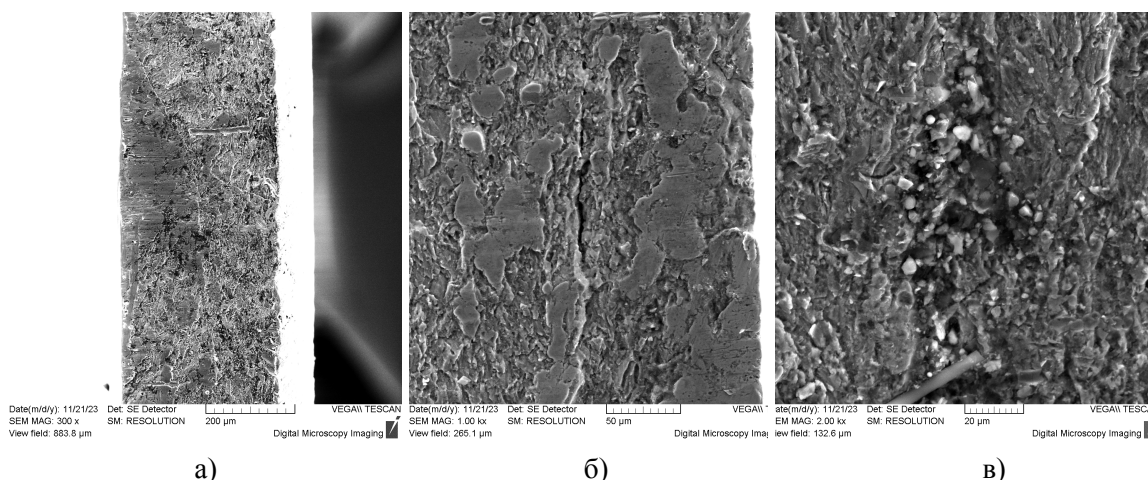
Микрофотографии излома образца: а) очаг разрушения; б) трещина; в) частицы карбидов
